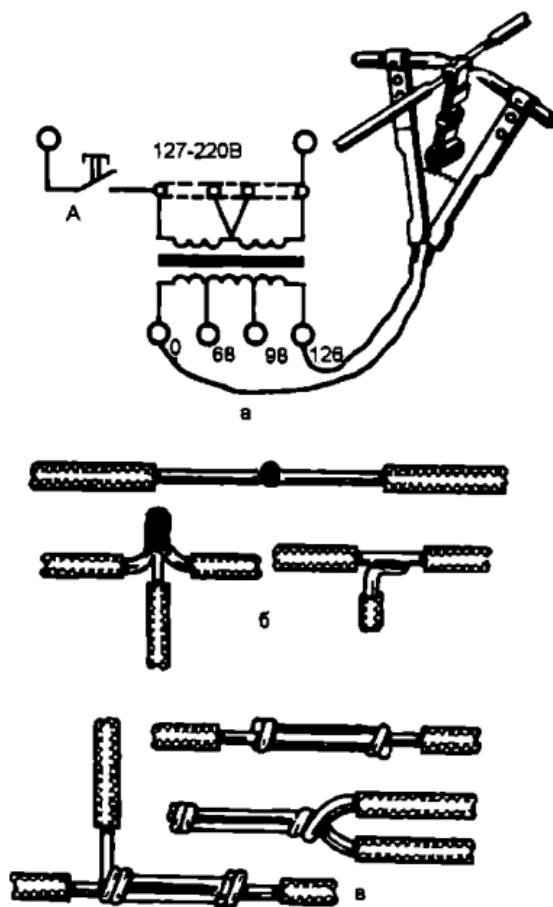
Соединение проводов сваркой и пайкой:
